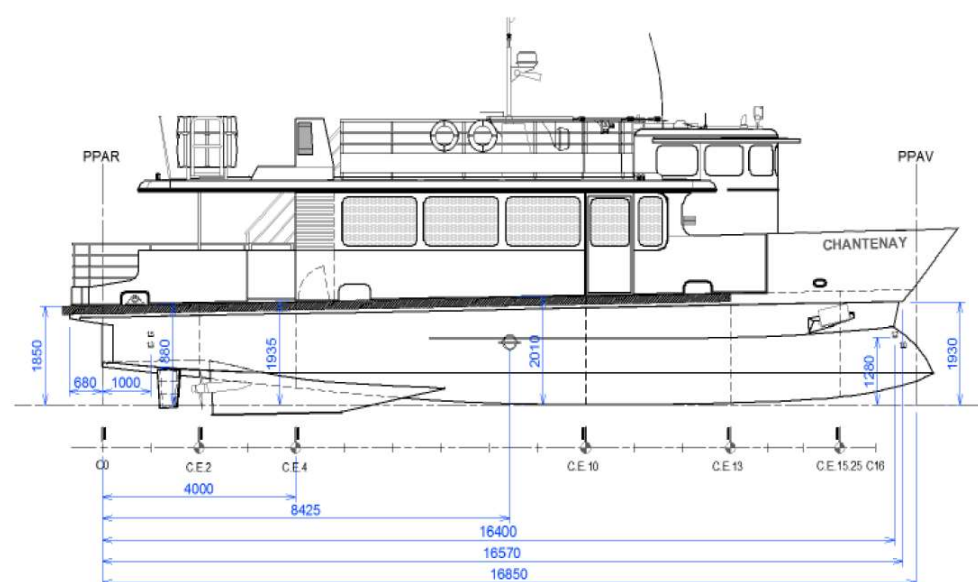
Plan d'un navire type – Source : SCE, décembre 2023
